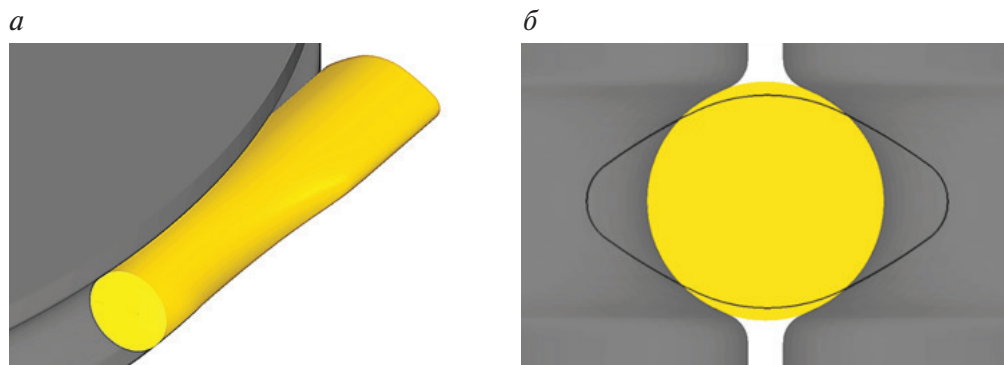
Пример постановки и решения задачи прокатки измененной заготовки в круглом калибре:
